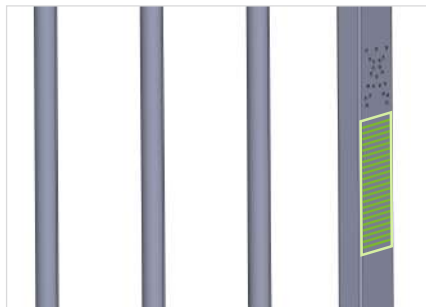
Зона с отверстиями для крепления считывателей
